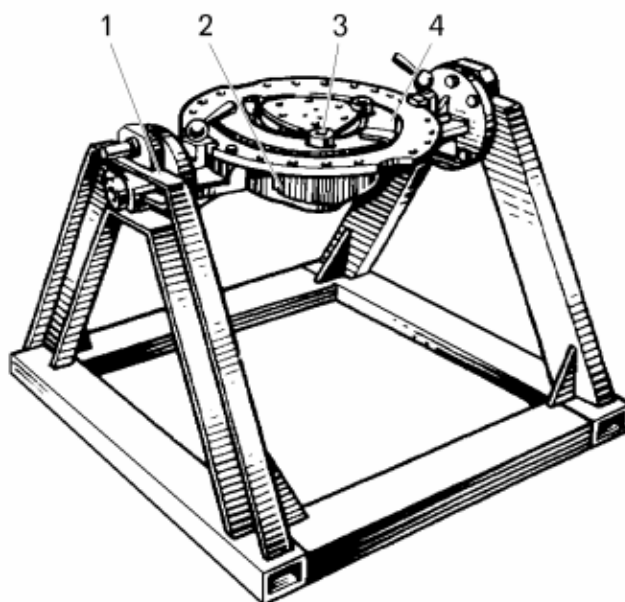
Стенд для сборки и разборки водила колесной передачи:
